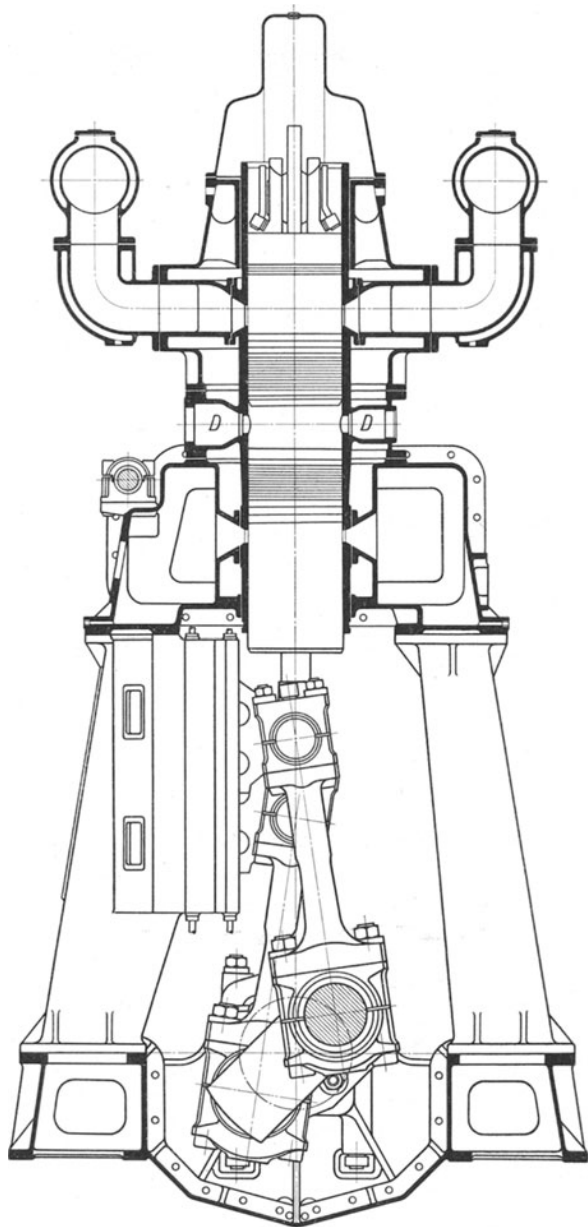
Schnitt durch Arbeitszylinder, Auspuffleitungen und Spülluftaufnehmer einer Junkers-Ölmaschine.
